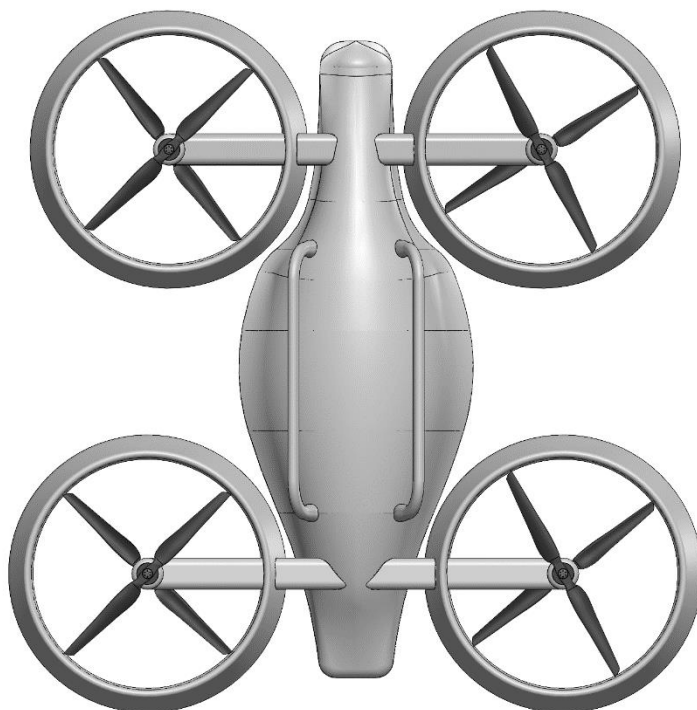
Vista planta inferior. Fuente: elaboración propia.
